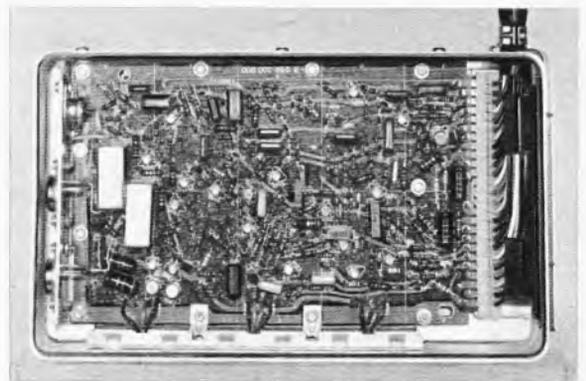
Blick in das geöffnete Steuergerät für die elektronische Benzineinspritzung (Werkaufnahme: Bosch)
